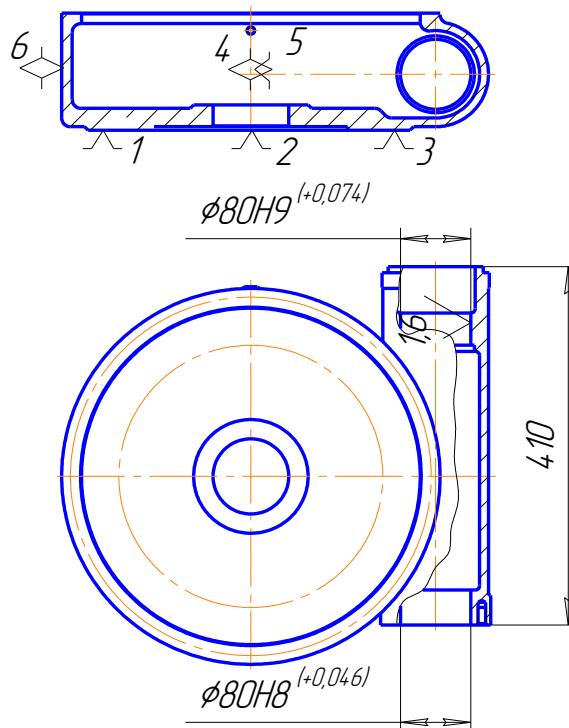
Ескіз обробки поверхні  $\varnothing 80H8^{(+0,062)}$
